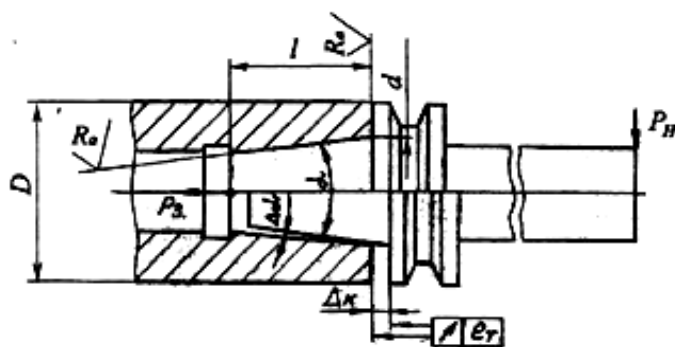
Схема соединения с двумя базирующими поверхностями
